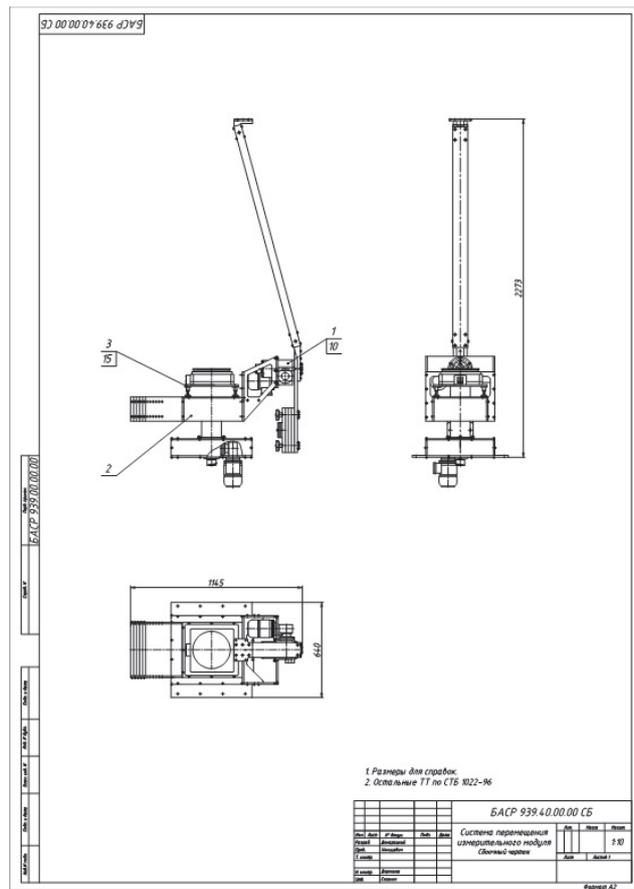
а. Габаритный чертеж; Рисунок 5б. Сборочный чертеж; Рисунок 5в. Система сканирования измерительного блока
